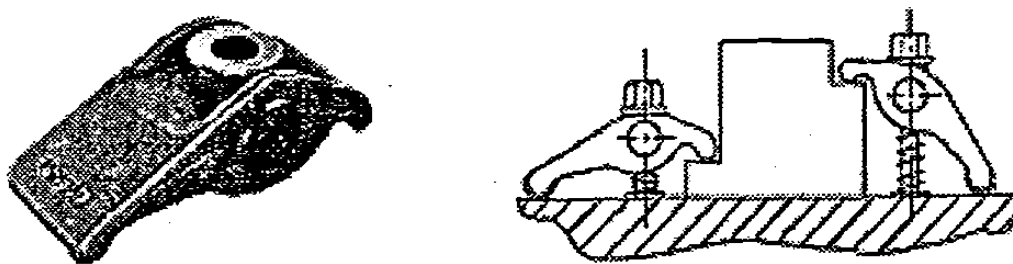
Las grapas ajustables forjadas tienen un apoyo incorporado de talón.
